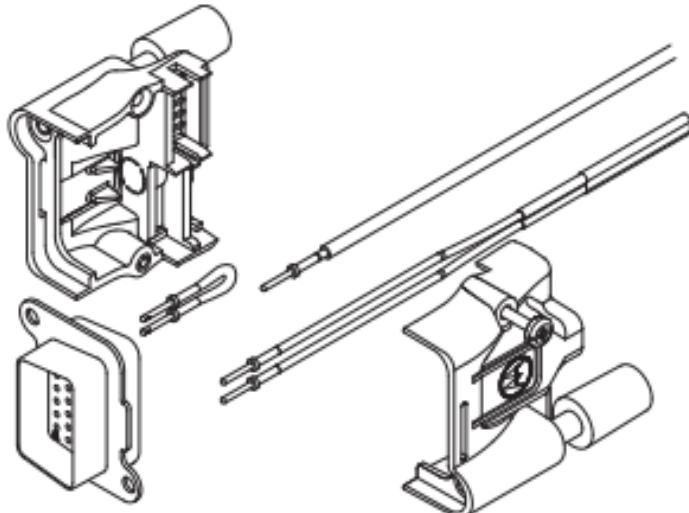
Разобранный вид соединительной колодки для аксессуаров APX
